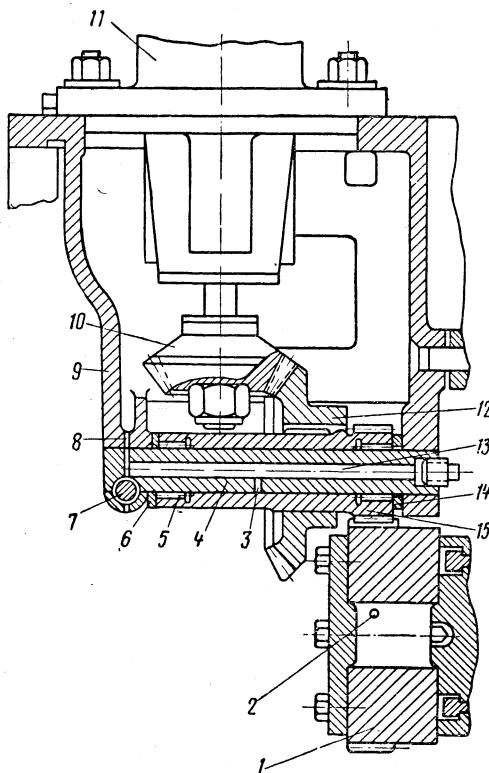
Привод регулятора числа оборотов вала дизеля 2Д50:
